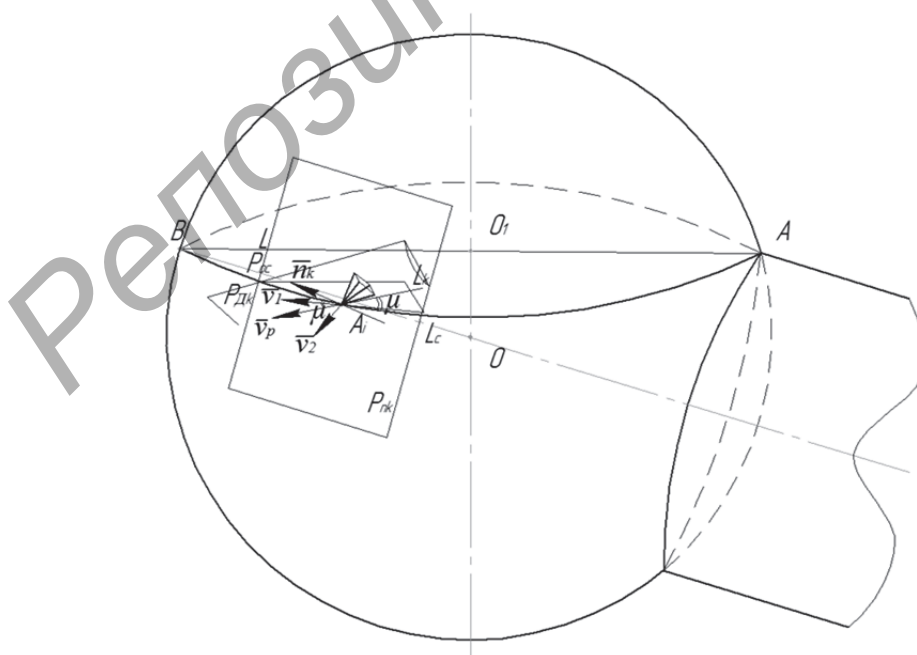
Главные статические и кинематические углы лезвия инструмента на сферической поверхности с учётом движения инструмента и заготовки
